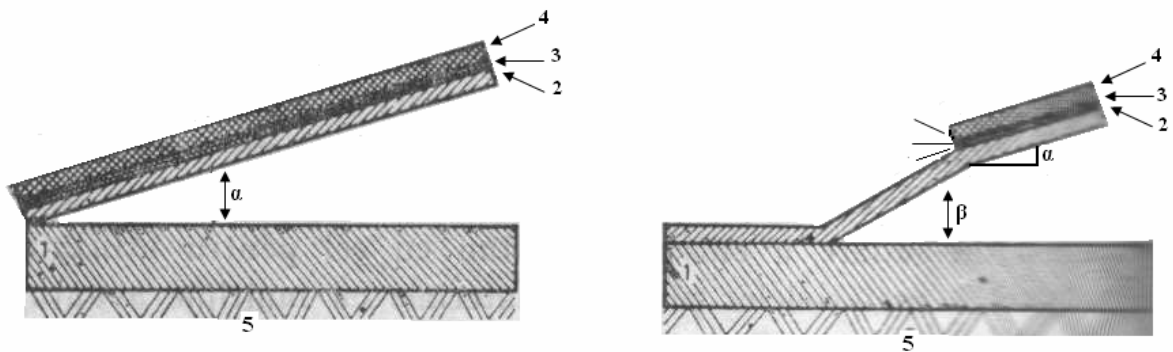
Dispoziție în diedru a componentelor de sudat: 1 - placa de bază; 2 - placa de adaos; 3 - amortizor; 4 - șarjă explozivă; 5 - dispozitiv suport.
